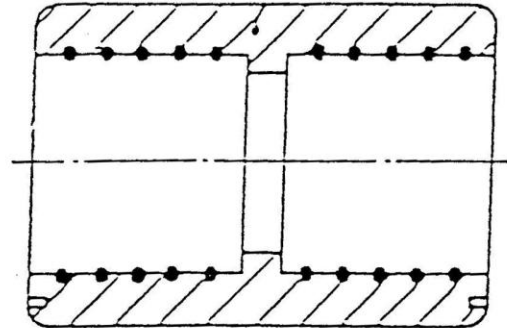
Ηλεκτροσυγκόλληση (Electrofusion Welding)
